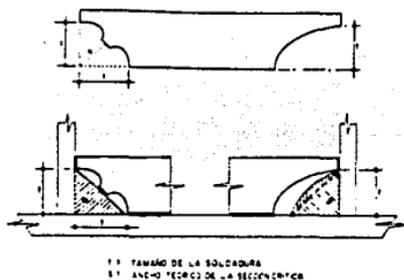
a) Calibradores para medir el tamaño de la soldadura.
